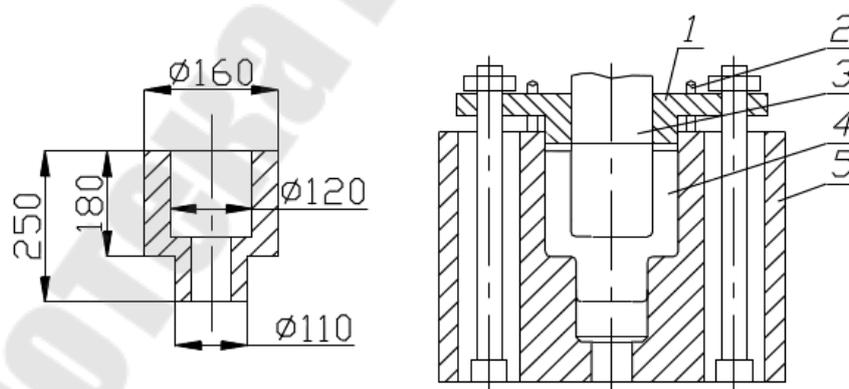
Штамповка поковок ползуна и корпуса из жидкого металла:
